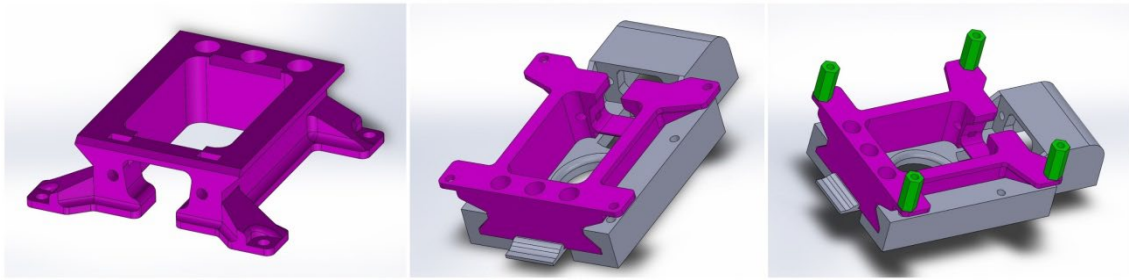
Diseño en 3D de la pieza específica de soporte para gimbal multiposición.
